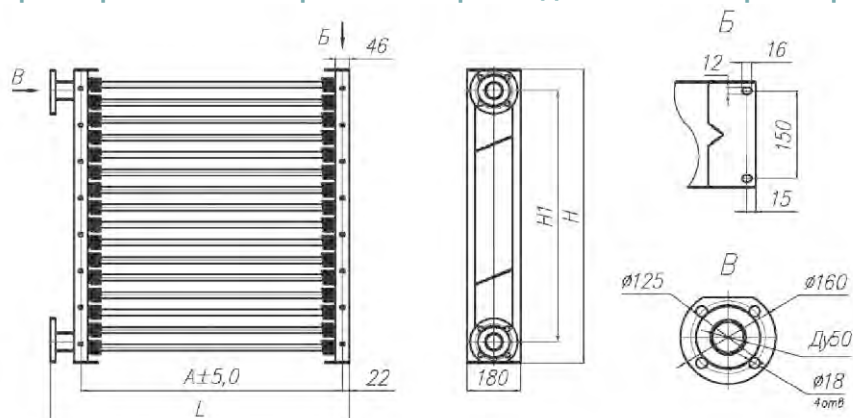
Габаритные и присоединительные размеры ТБЗ-.....22.
